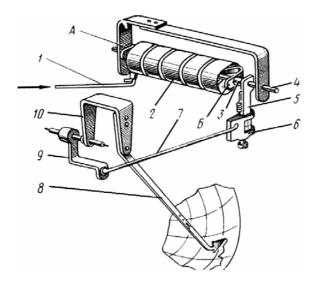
Манометр с многовитковой трубчатой пружиной: 1 -капиллярная трубка; 2 -пружина; 3 -втулка; 4 -ось; 5 -рычаг; 6 -каретка; 7 -тяга; 8 -держатель пера; 9 -мостик; 10 -поводок; A, E -концы пружин
